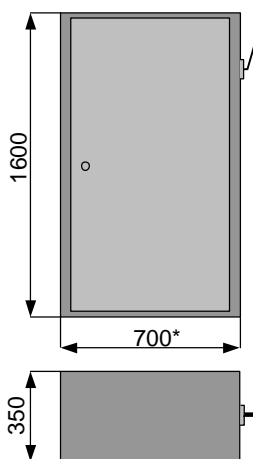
Общий вид и габаритные размеры шкафов ШРС, ШР 11:
